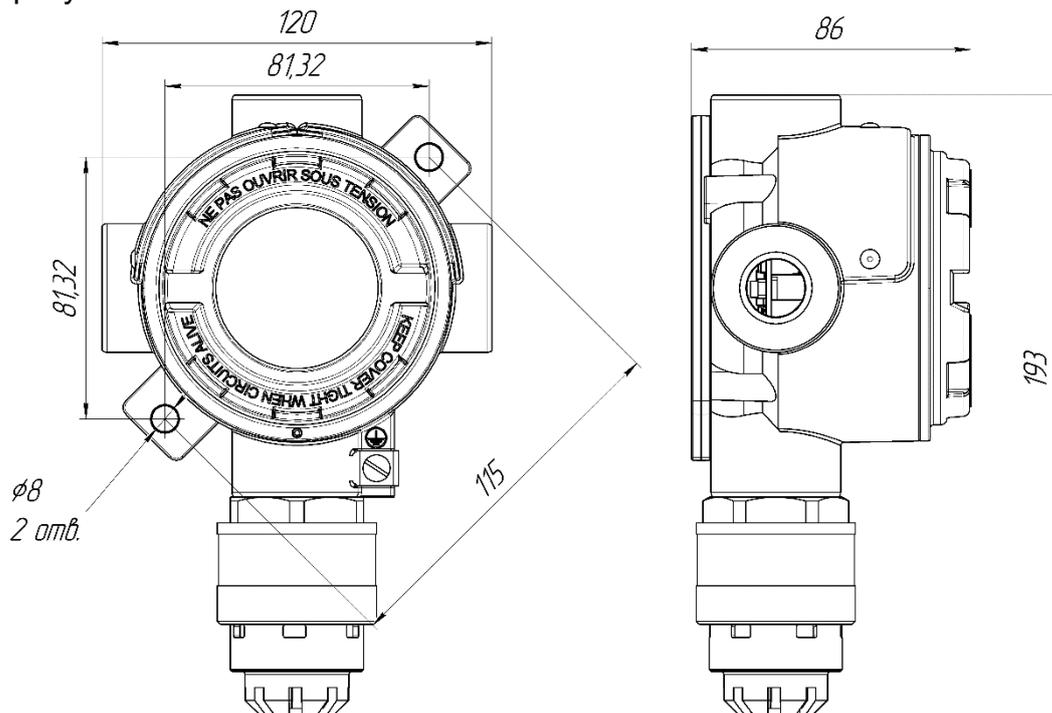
Габаритные размеры ДГС ЭРИС-210
